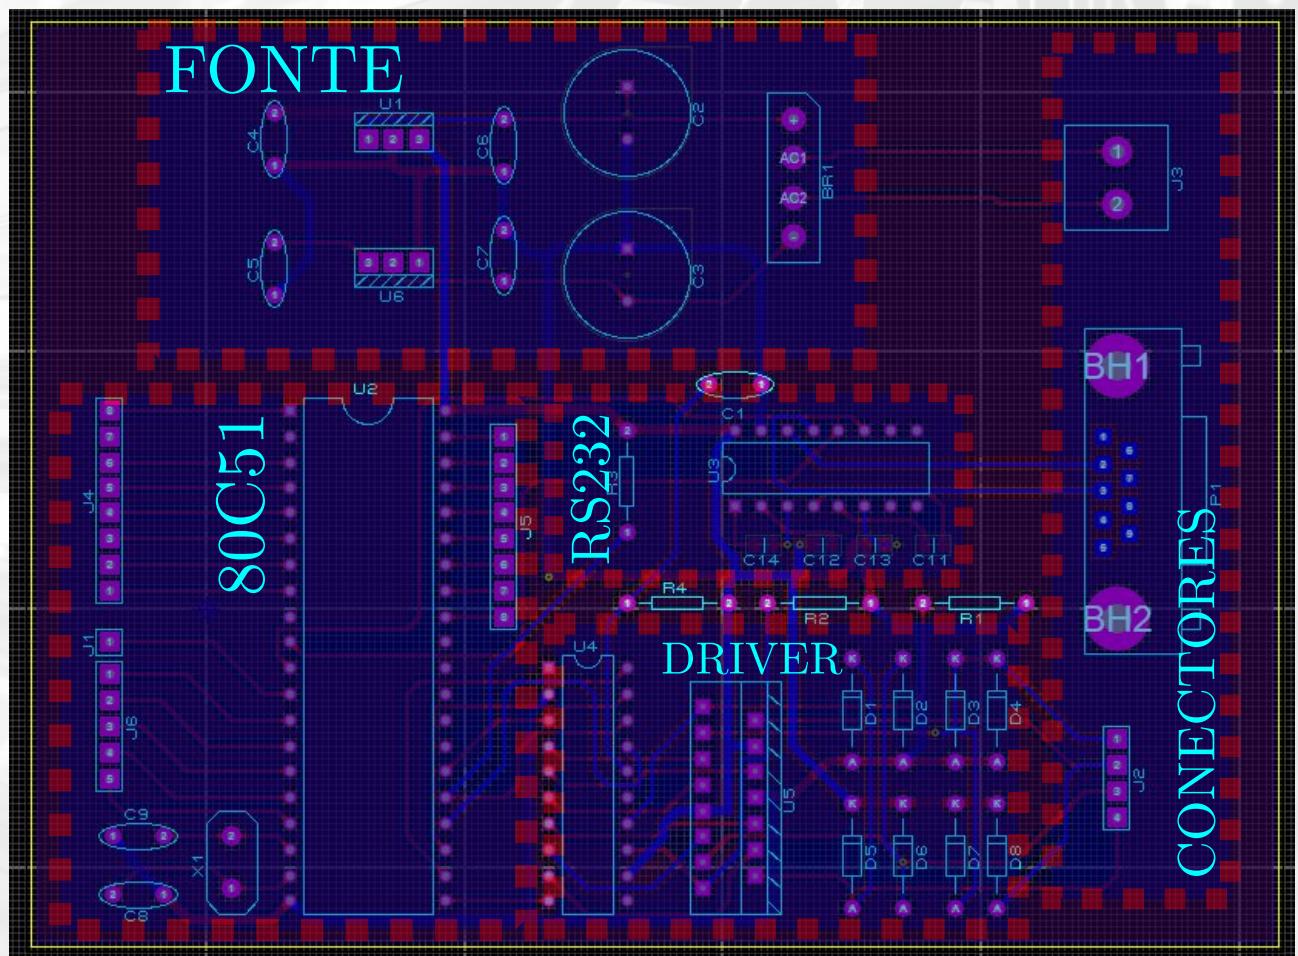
PCB com Indicações do Posicionamento de Cada Bloco de Execução
